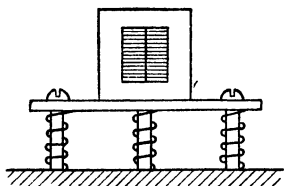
Регулировочное приспособление для установки положения магнитной головки.
